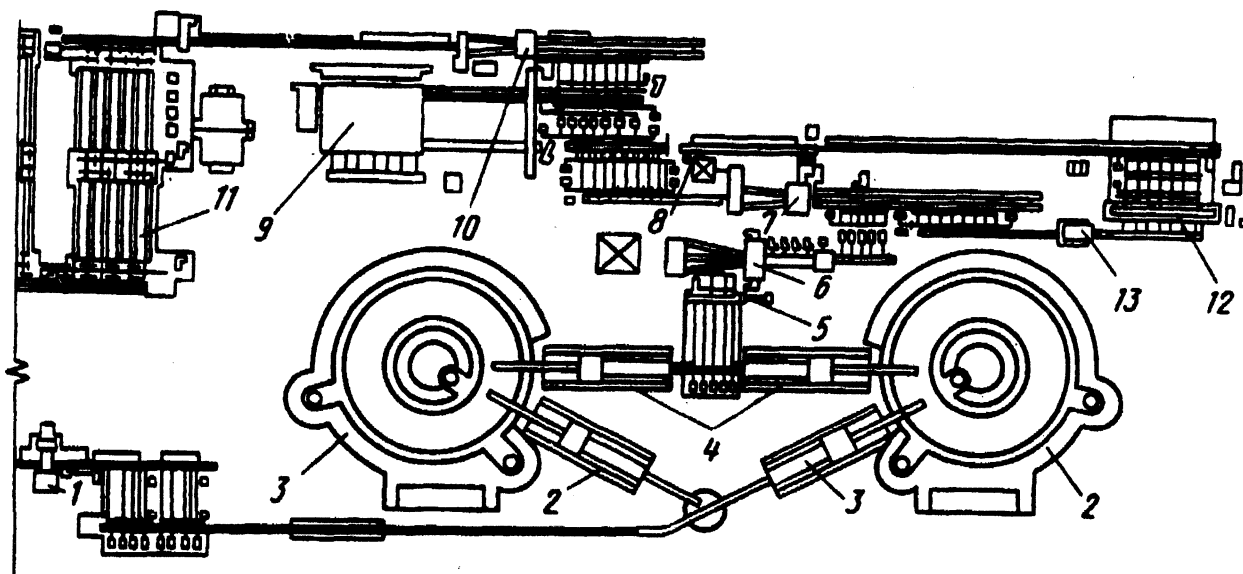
Схема расположения оборудования в агрегате с трехвалковым станом поперечно-винтовой прокатки: 1 – пресс для резки заготовки; 2 – машина для загрузки заготовок; 3 – кольцевая печь; 4 – машина для выдачи заготовки; 5 – зацентрировщик; 6 – прошивной стан; 7 – стан поперечно-винтовой прокатки; 8 – оправкоизвлекатель; 9 – подогревательная печь с шагающим подом; 10 – калибровочный стан; 11 – охлаждающий стол; 12 – ванна для охлаждения оправок; 13 – машина для смазки оправок
